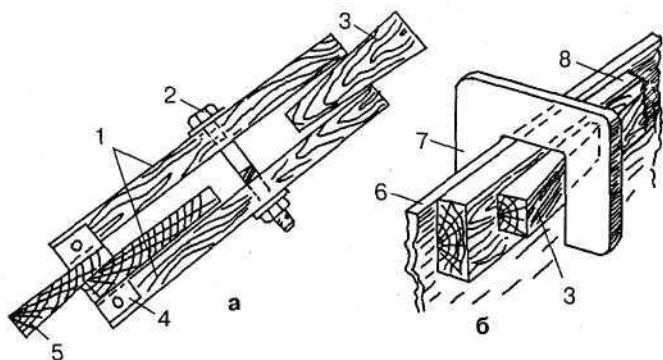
Клещи (а) и цвинка (б): 1 — бруски; 2 — болт; 3 — клин; 4 — кусочки кожи; 5 — наборная обшивка; 6 — обшивка; 7 — зажим; 8 — привальный брус
